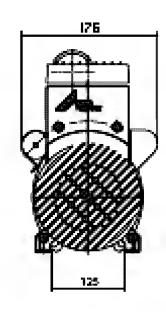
Габаритные и присоединительные размеры компрессора D-100
